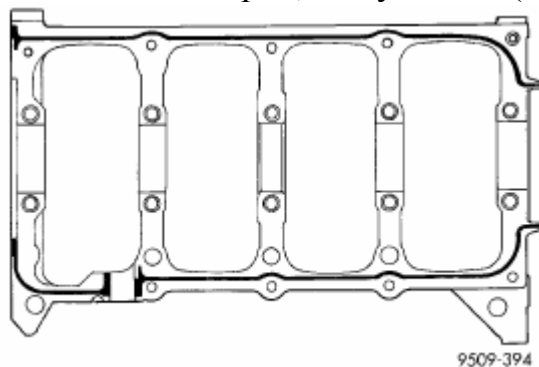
Уплотнение блока и крышки коренных подшипников.
